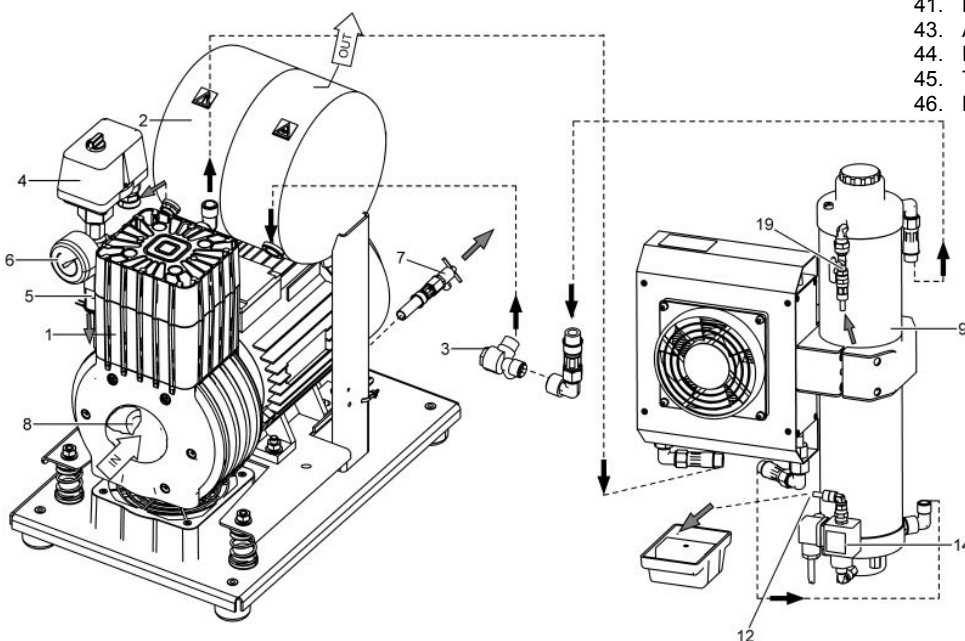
Kompressor mit Lufttrockner MONZUN- M1a
